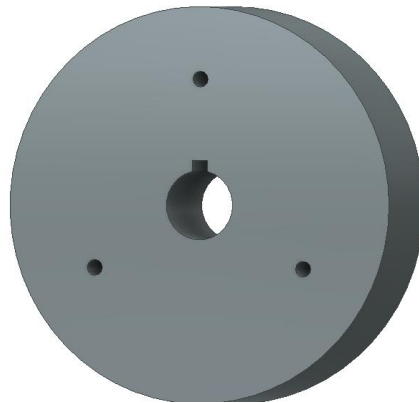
Útil de mecanizado de muñones de cigüeñal.
